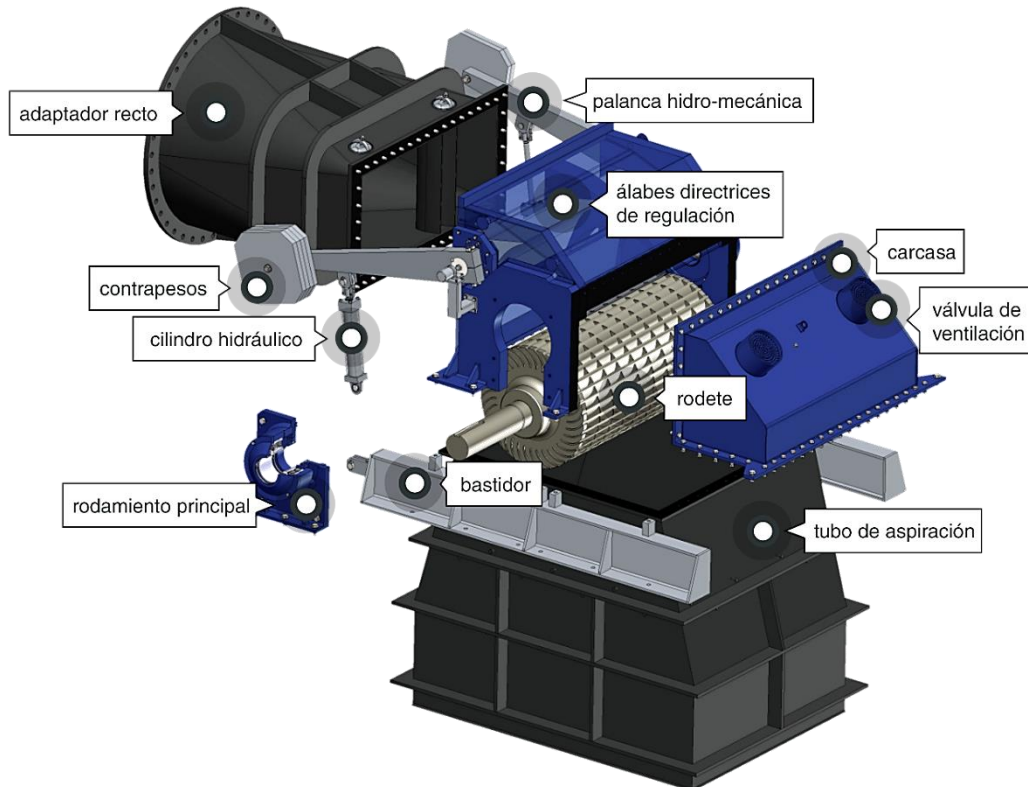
Esquema de una turbina Ossberger. Fuente: Fabricante Ossberger
